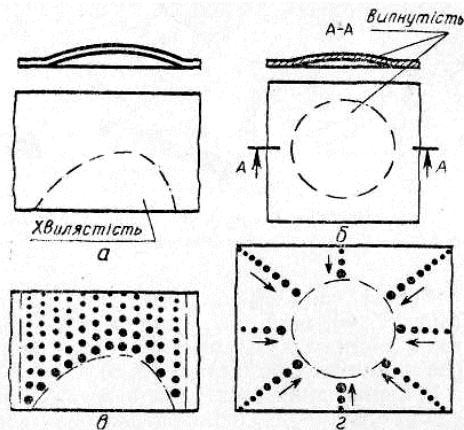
Зігнуті заготовки з листового металу (а, б) і схеми їх випрямляння (в, г)
